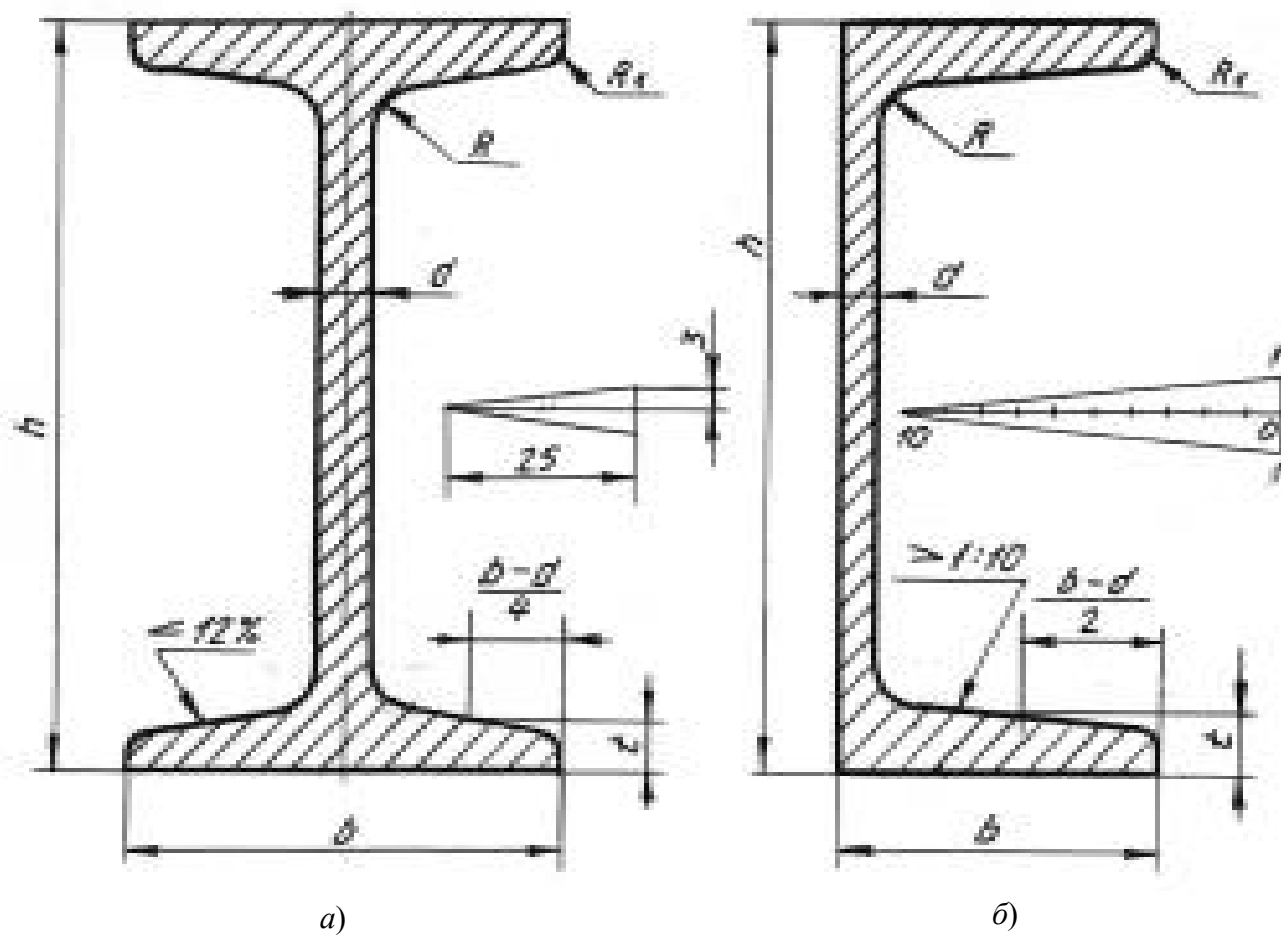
Профили проката: а) двутавровая балка; б) швеллер
